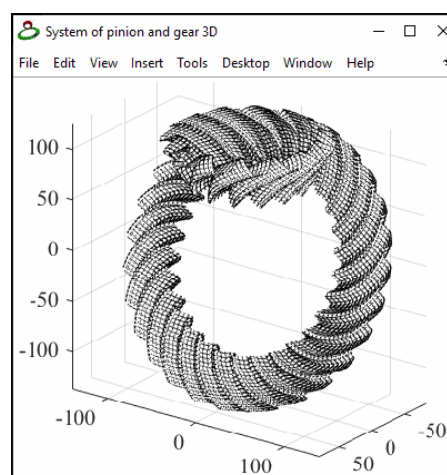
Сопряженные поверхности зубчатых венцов спиральной конической передачи
